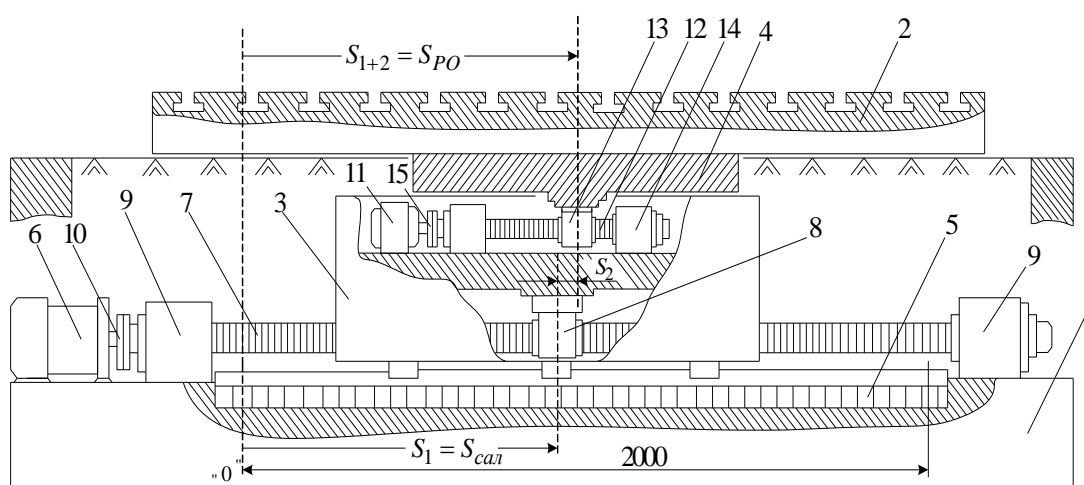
Упрощенная схема конструкции двухдвигательного безредукторного МП с двумя винтовыми парами для продольной подачи РО металлорежущего станка
